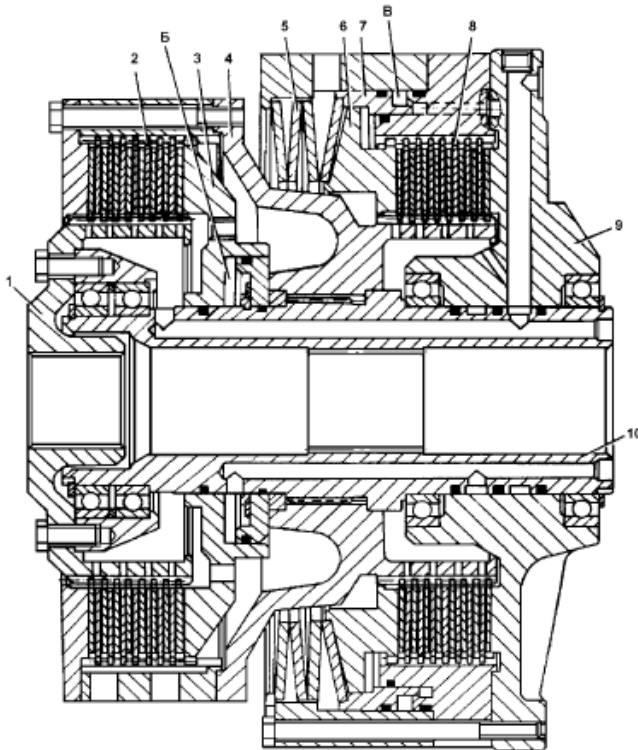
Бортовой фрикцион и остановочный тормоз:
